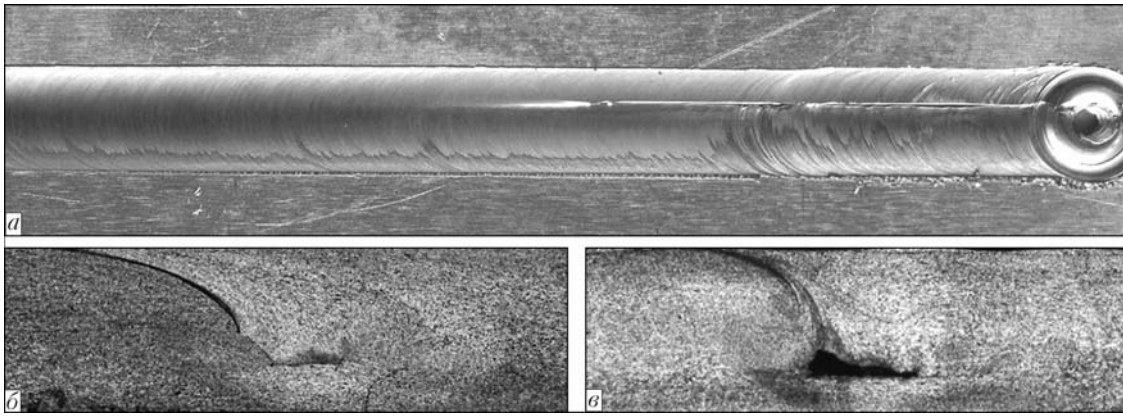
Внешний вид лицевой поверхности шва (а, X1,4), полученного СТП при сборке стыка с переменным зазором (0,2...1,2 мм) между кромками, и поперечные макрошлифы сварных соединений сплава АМг2 толщиной 2 мм при зазоре 0,3 (б) и 0,5 мм (в)
